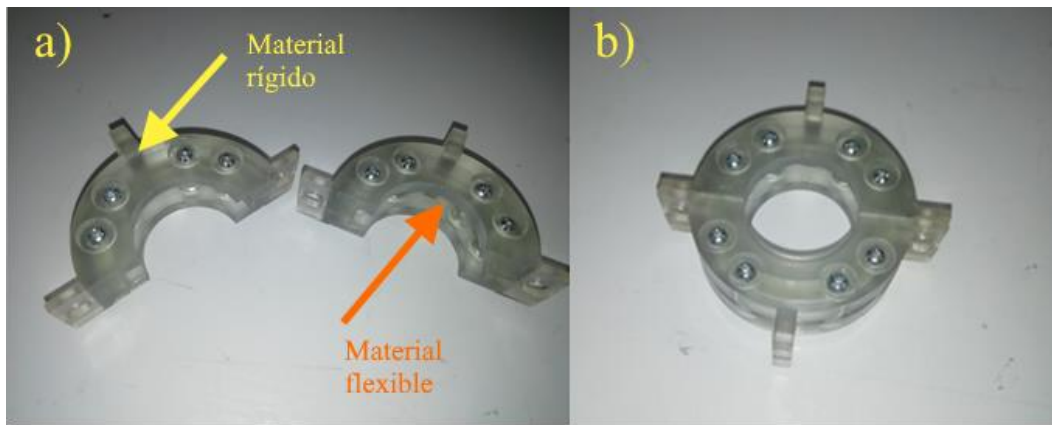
Fabricación de las bridas mediante manufactura aditiva.
